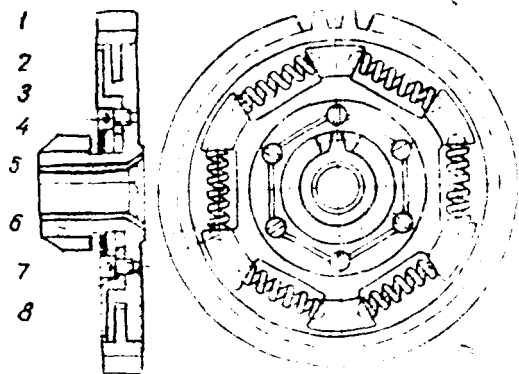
Двойная шестерня привода механизма газораспределения: 1—Большой венец; 2—фланец; 3—крышка; 4—винт; 5—втулка; 6—малый венец; 7—пружина; 8—сухарик
